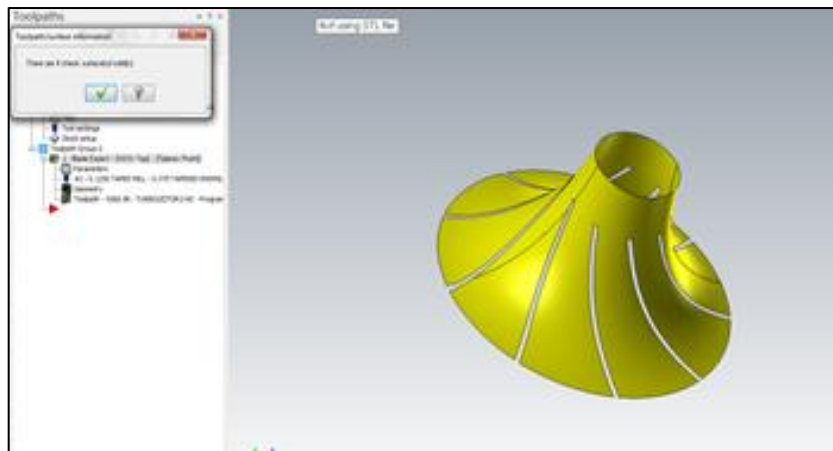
Enlace del maquinado para el cuerpo del turbo [fuente propia]
